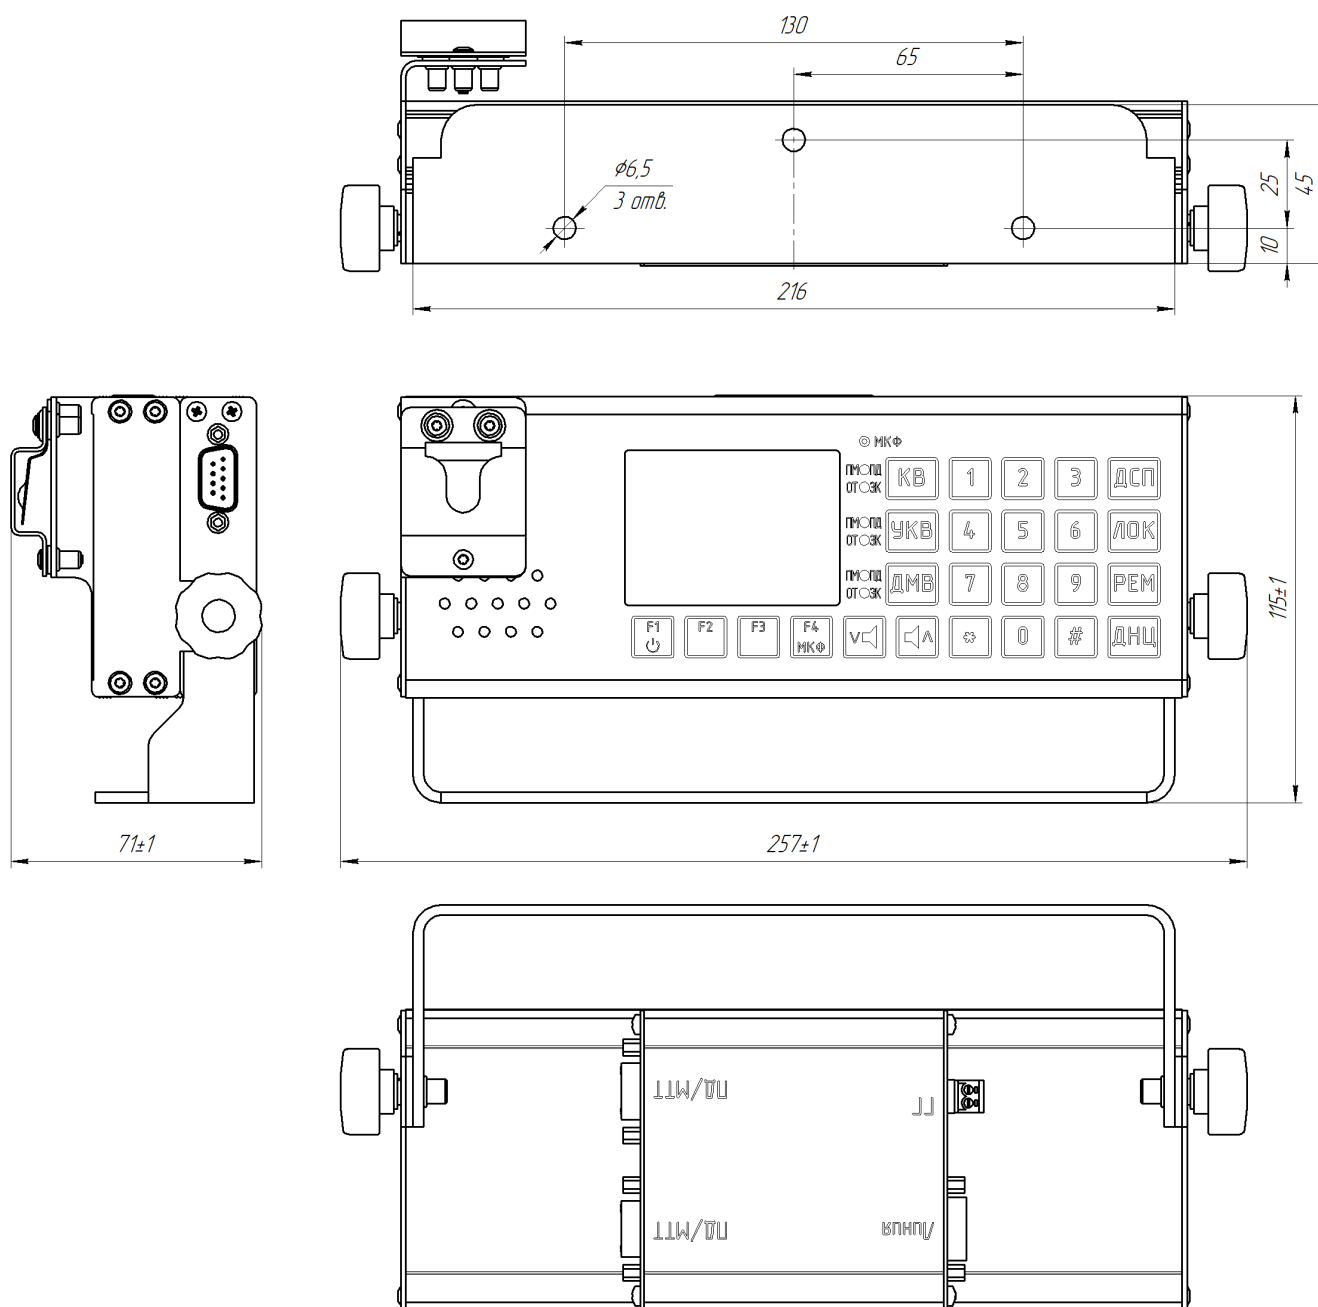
Габаритные и установочные размеры ПУ
